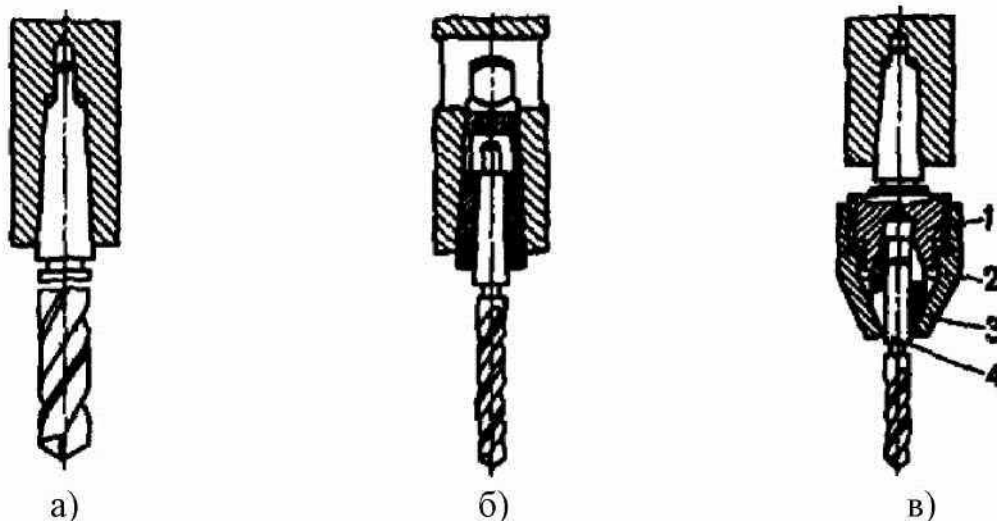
Схеми закріплення інструменту на свердлильних верстатах
